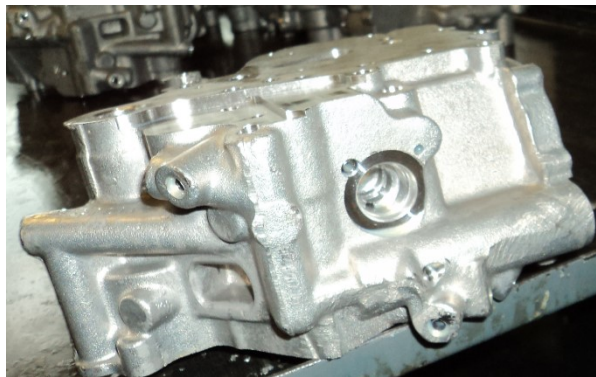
Загальний вигляд корпусної деталі гідроапаратури
